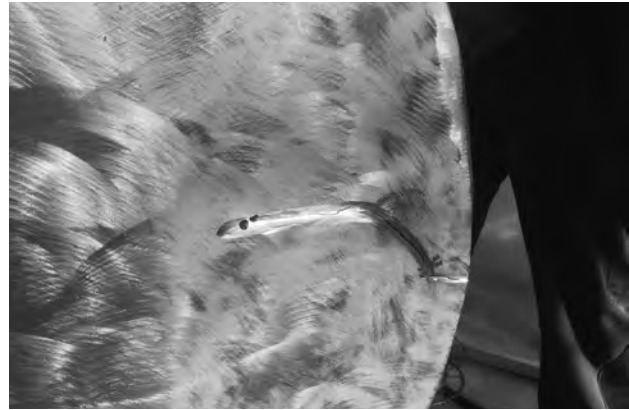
, г. Локализованная методом засверливания трещина, подготовленная для начала сварочных работ
